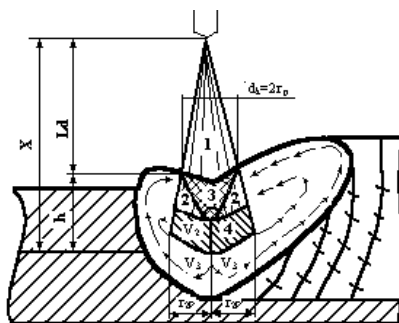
Принципиальная схема движения расплава в сварочной ванне
